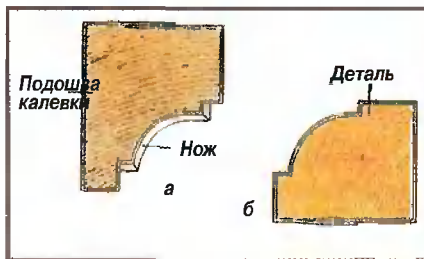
Форма подошвы и ножа калевки (а) и профиль обработанной детали (б).
